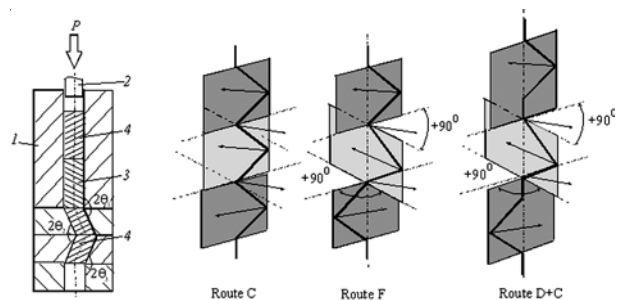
Схемы процесса и маршрутов РКМУЭ: 1 – матрица; 2 – плунжер; 3 – полимерная заготовка и 4 – фальш-заготовка
